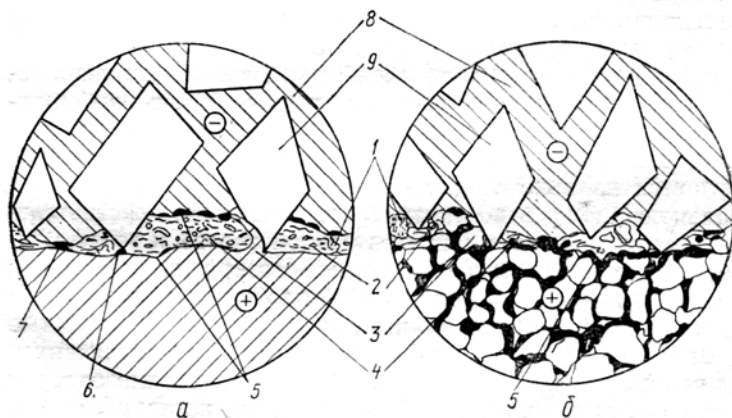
Схема зоны контакта «круг - обрабатываемая деталь» для пластичного (а) и хрупкого (б) материалов:
